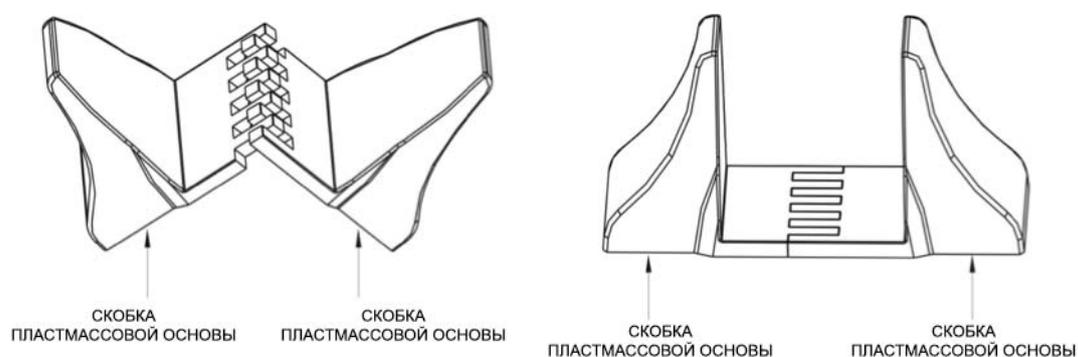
Сборка пластмассовой основы аккумуляторного блока 1 кВА
